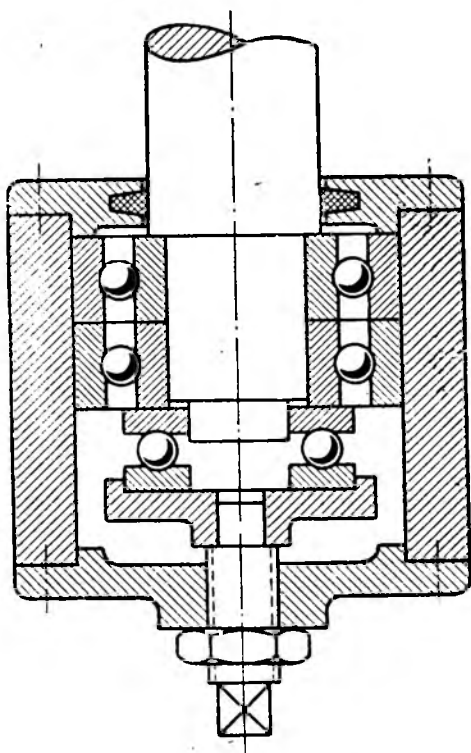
Схема расположения радиального подшипника на одношпиндельном фрезерном станке
